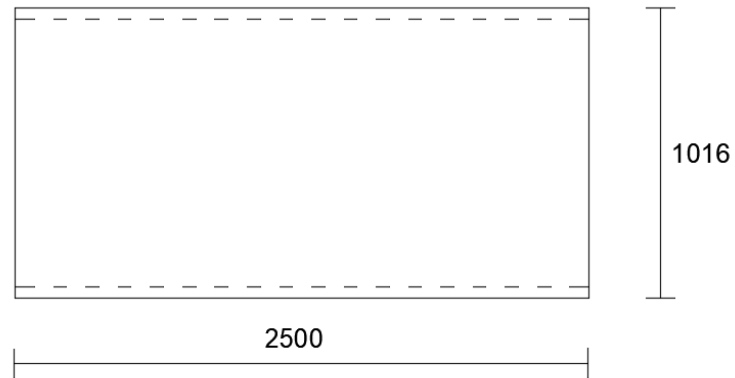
Dimensiones de la carcasa cilíndrica exterior del depósito PHV-004. Fuente: propia
